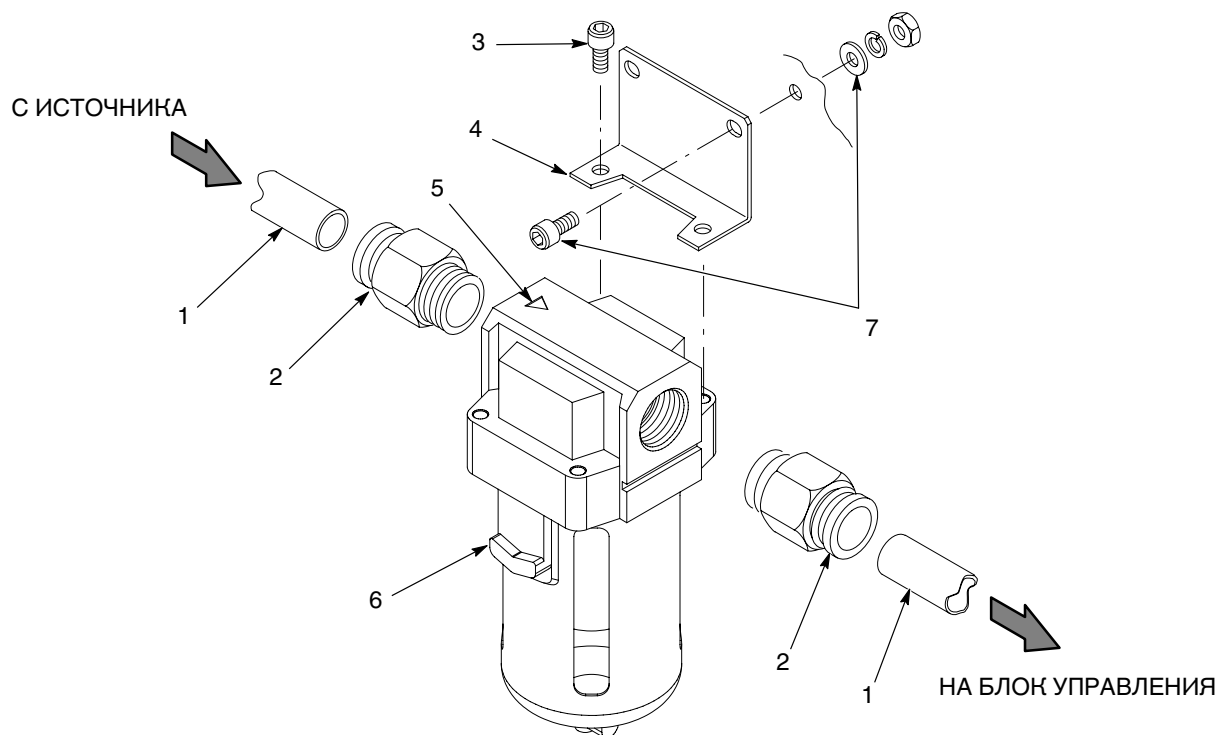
Монтаж воздушного фильтра — системы для монтажа на стене и на поручне
